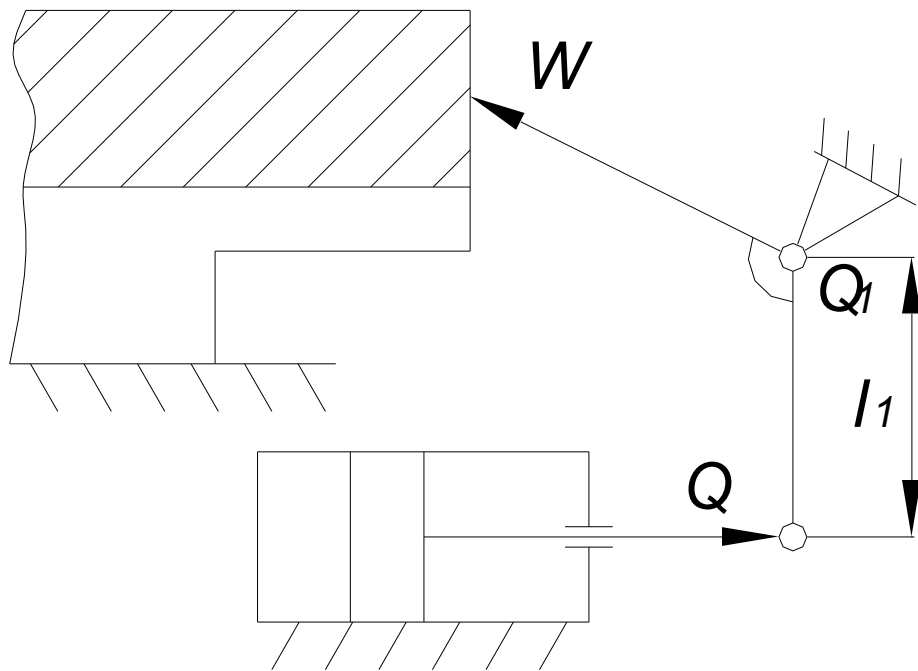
Схема компоновки пристрою. II варіант.
